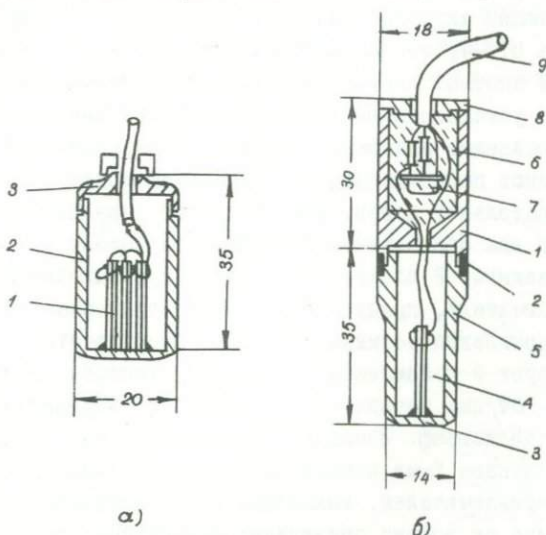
Схематические чертежи: а) излучатель: 1 - кристалл излучателя, 2 - герметизированный корпус, 3 - крышка; б) приемник: 1 - корпус усилителя, 2 - уплотнительное кольцо, 3 - рабочая плоскость приемника, 4 - пьезоэлемент, 5 - защитный экран пьезоэлемента, 6 - эпоксидная смола, 7 - усилитель, 8 - заглушка, 9 - коаксиальный ввод.
